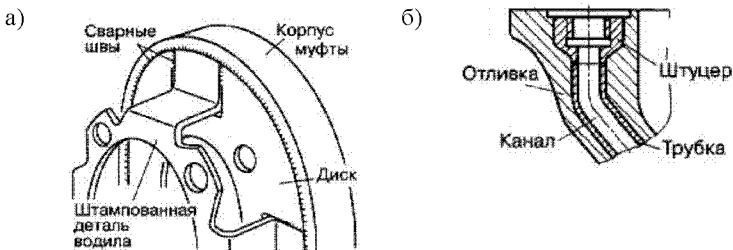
Конструктивные решения обеспечения технологичности изготовления детали
